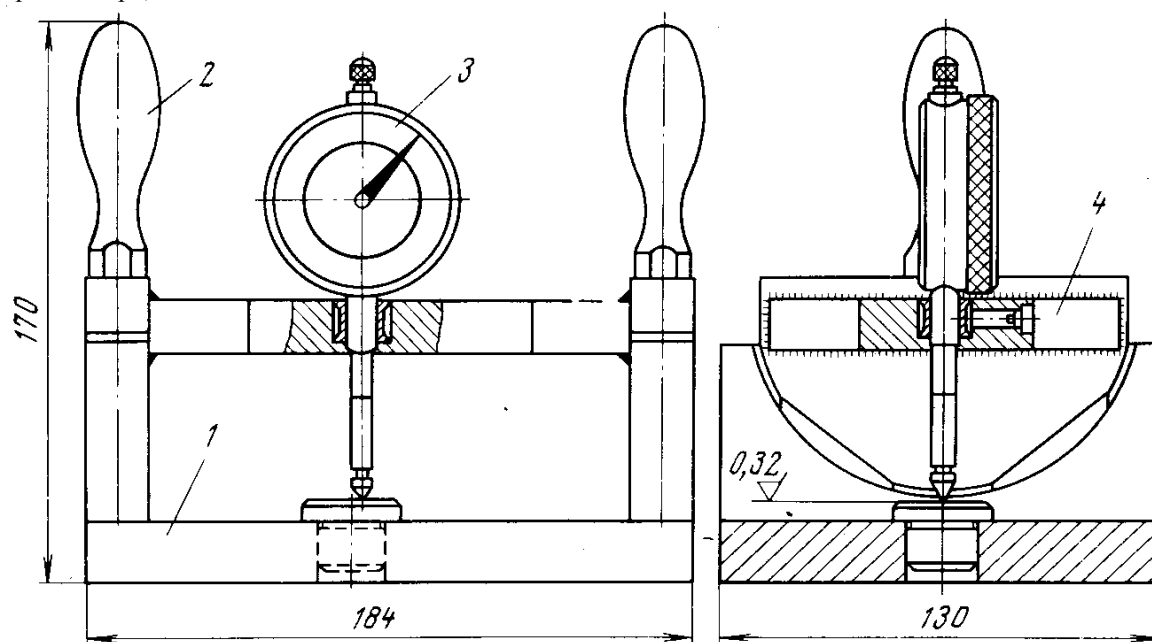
Контрольное приспособление для подбора толщины регулировочных шайб: 1 — корпус; 2 — ручка; 3 — индикатор; 4 — основание.
